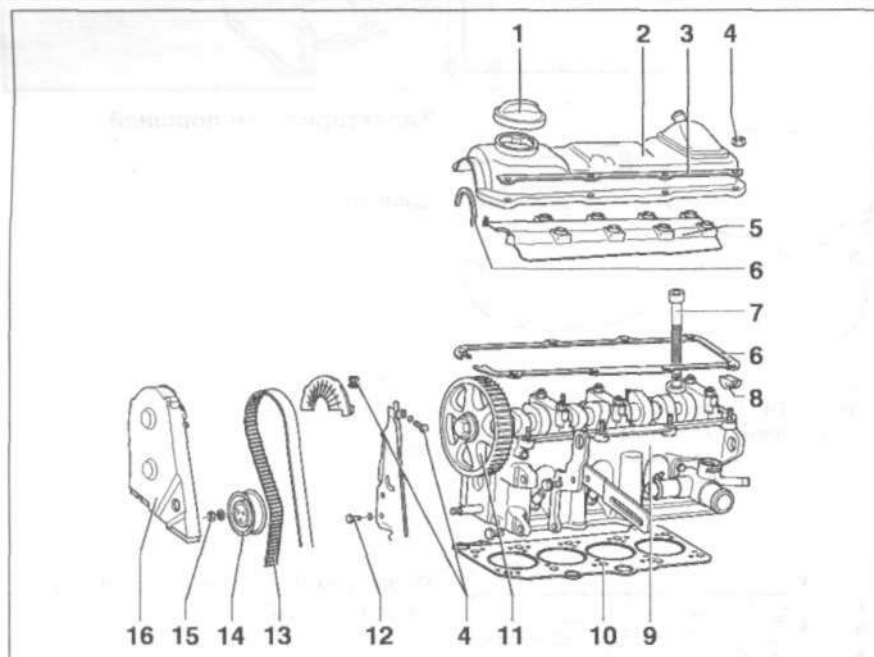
Головка блока цилиндров двигателей 1F и ADZ:
